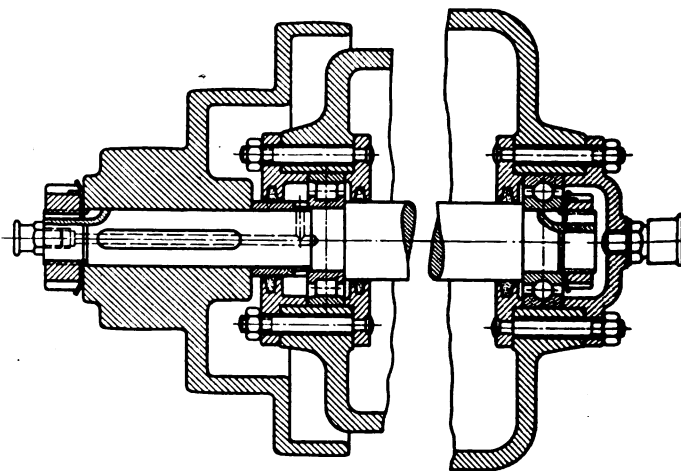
Zweideckelige Ausführung mit eingewinkelten Stiftschrauben, beim Ausbau Zerlegung des Rollenlagers.
